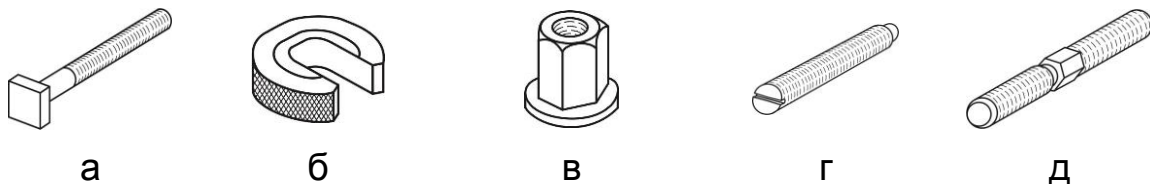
Приклади кріпильних елементів: а – пазовий болт; б – шайба швидкознімна; в – гайка; г – гвинт; д – шпилька
